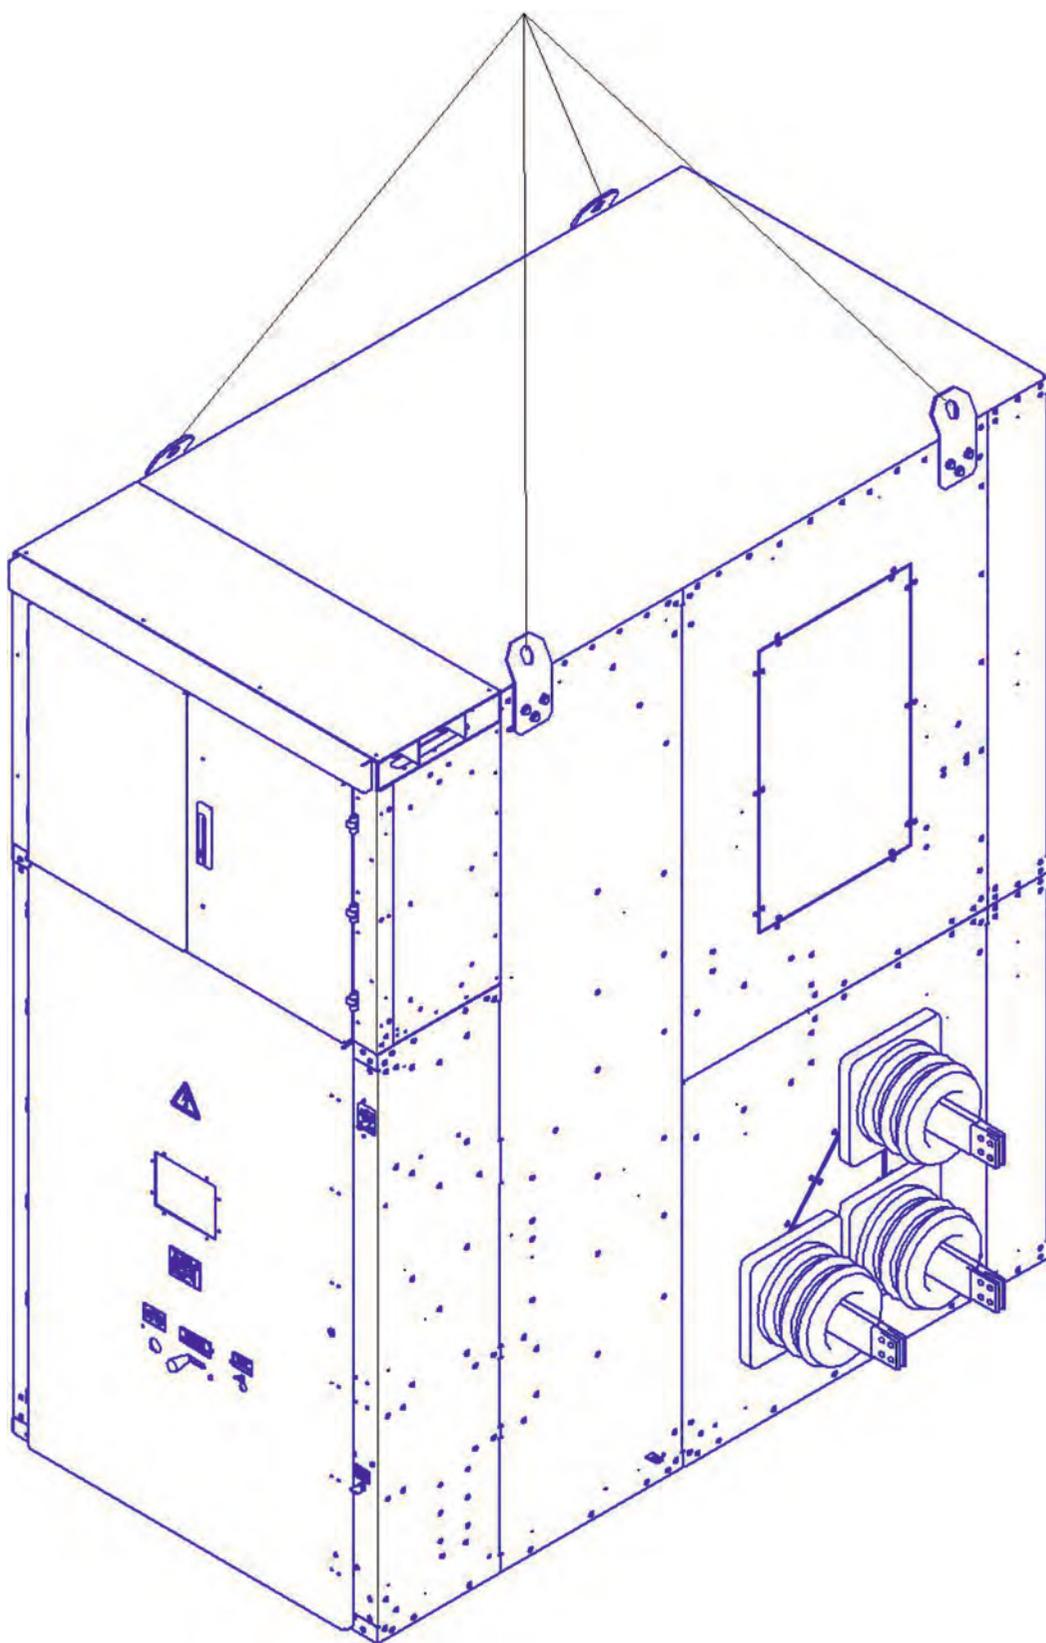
Подъем шкафа при перемещении в условиях цеха или монтажных площадок
